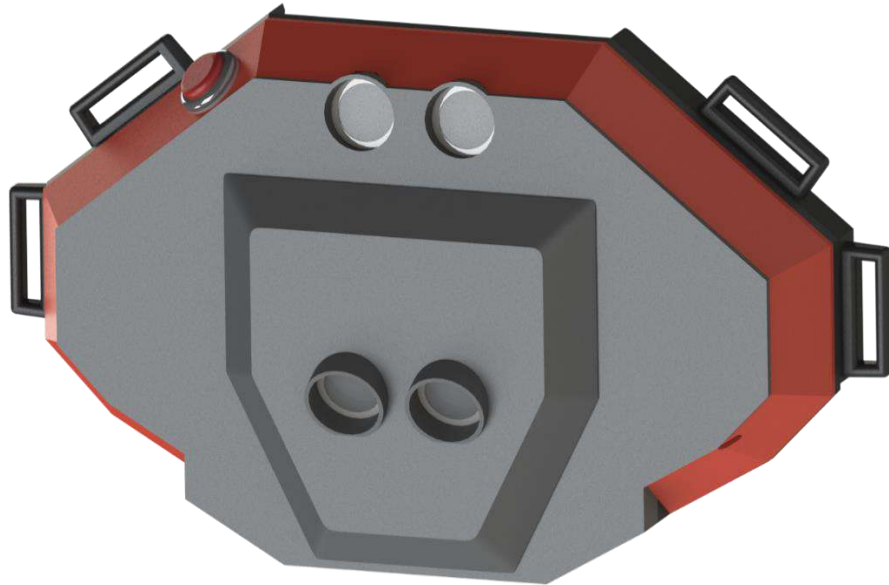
Модель корпусу пристрою, лицева сторона
